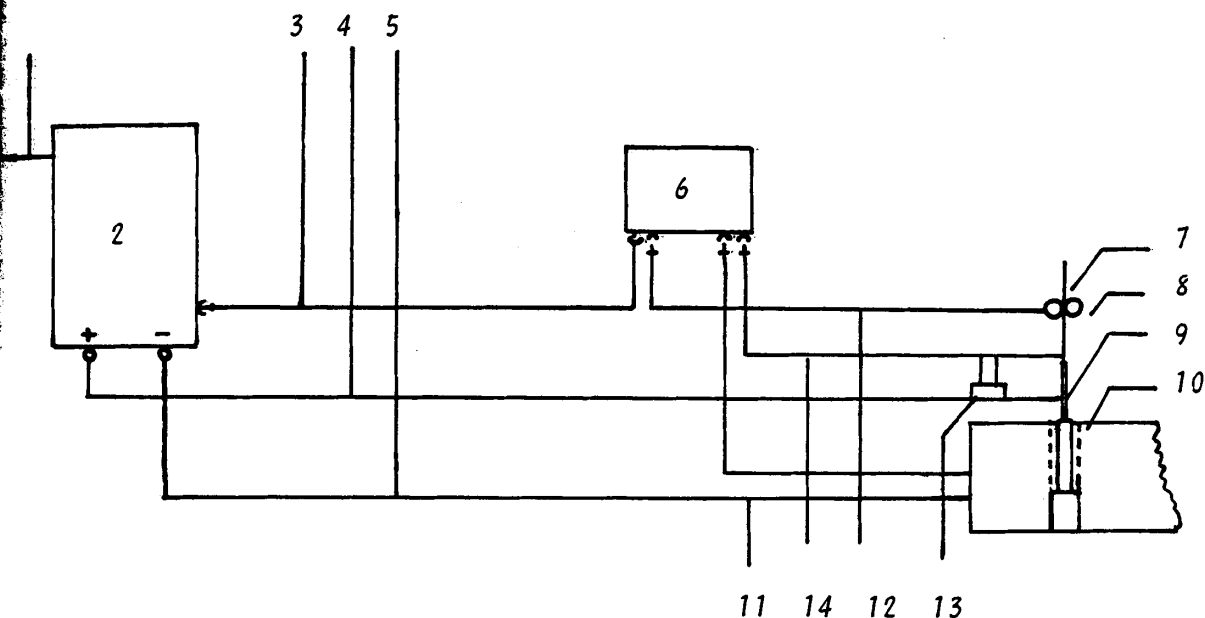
CONEXION ELECTRICA DE LA FUENTE DE PODER, CAJA, CONTROL Y CABEZAL DE SOLDADURA. (REF. 11).
